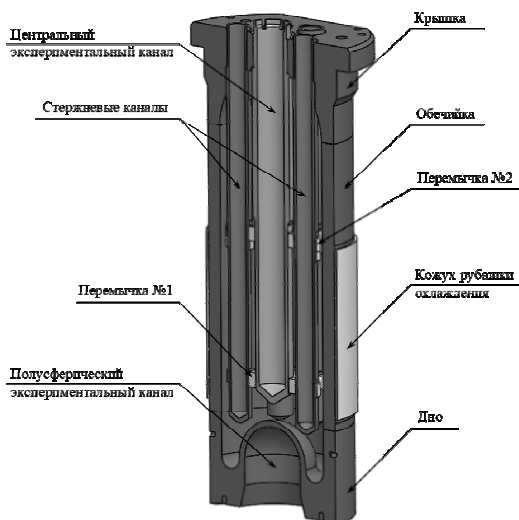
Конструктивная схема корпуса АЗ реактора ВИР-2М
